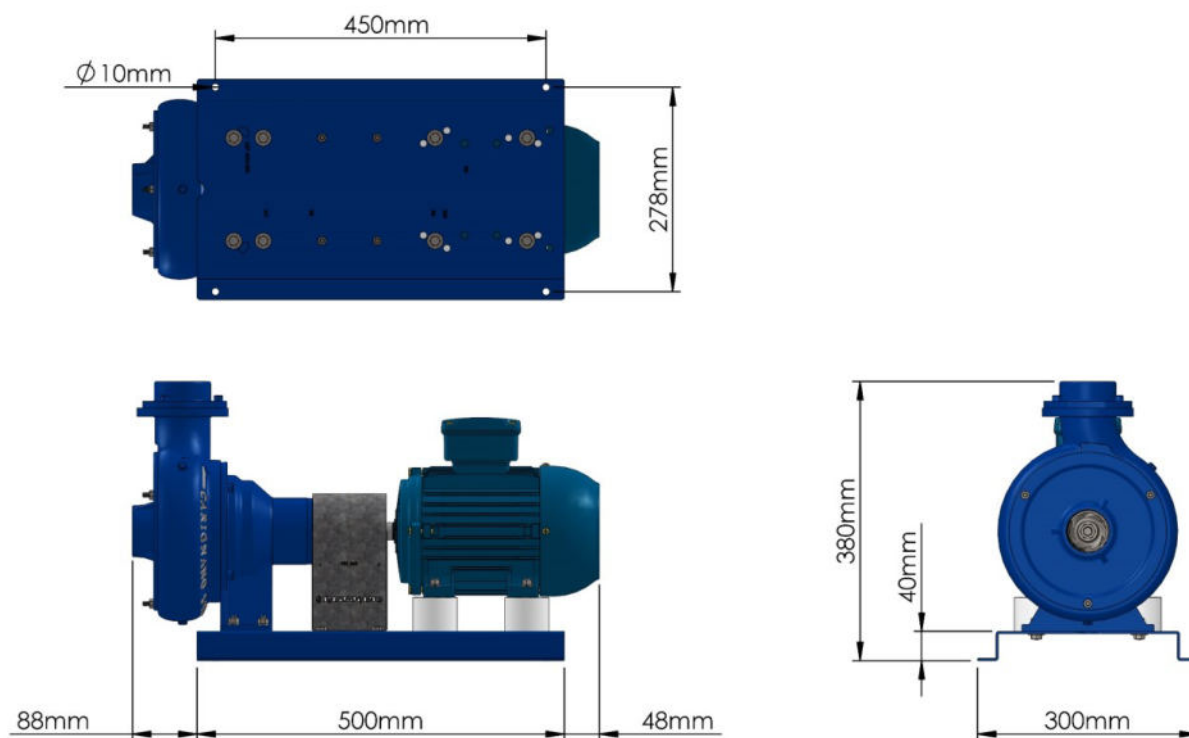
Dimensiones del conjunto Bomba + Motor + Acople mecánico + Base soporte.
